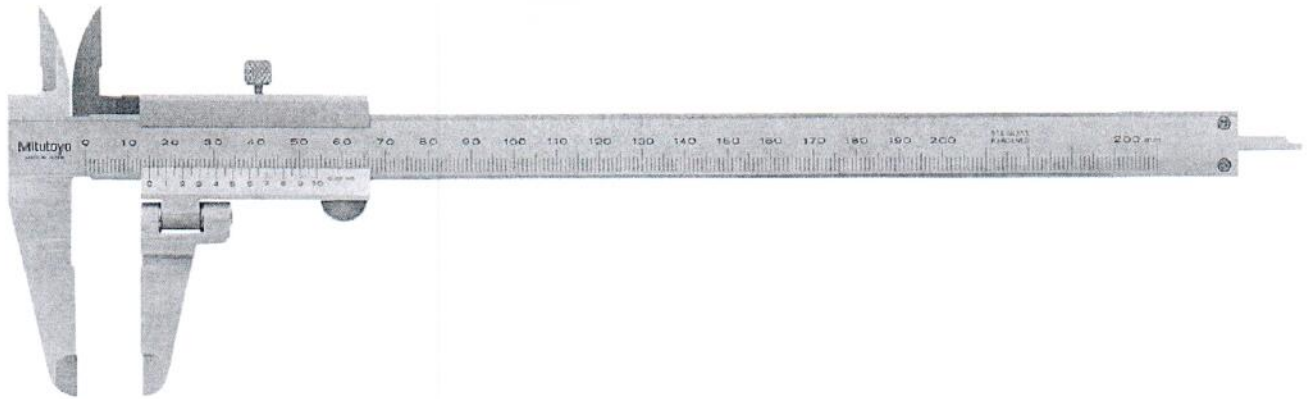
Внешний вид штангенциркуля серии 536 с поворотной губкой
